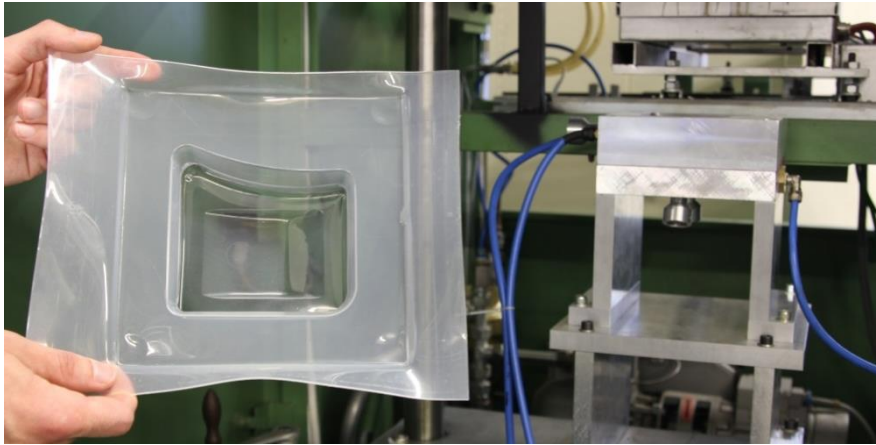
Prototypenwerkzeug des IKT zur Inline-Wanddickenmessung beim Thermoformen mittels Ultraschall
